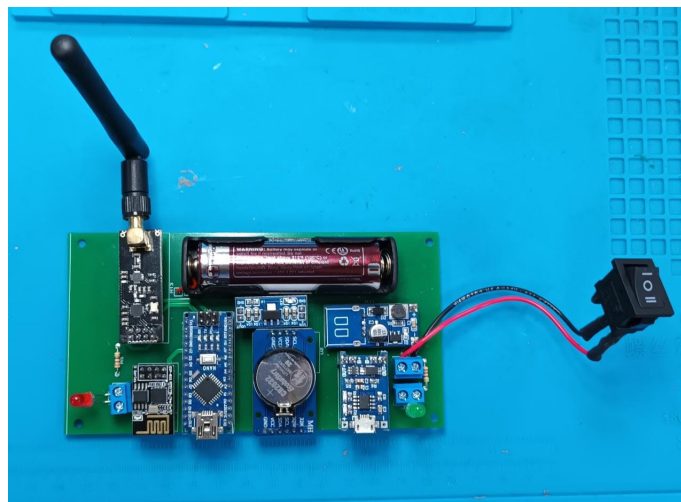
Montaje de componentes en PCB de nodo Gateway.
